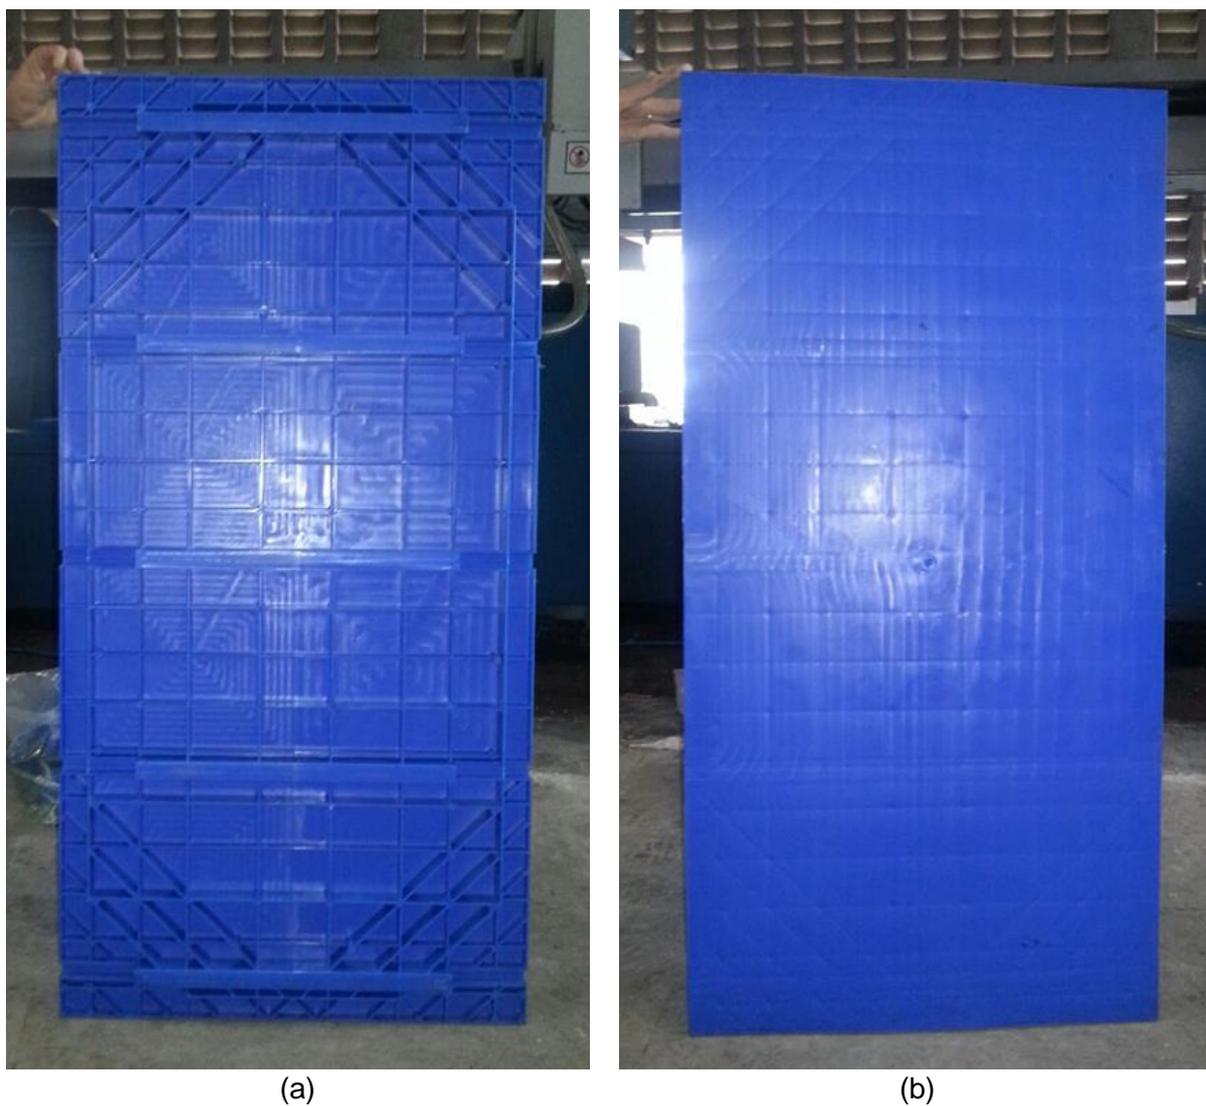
Plasterit* 122 x 61 cm fabricado (Versão 7) (a) Vista inferior; (b) Vista superior.
